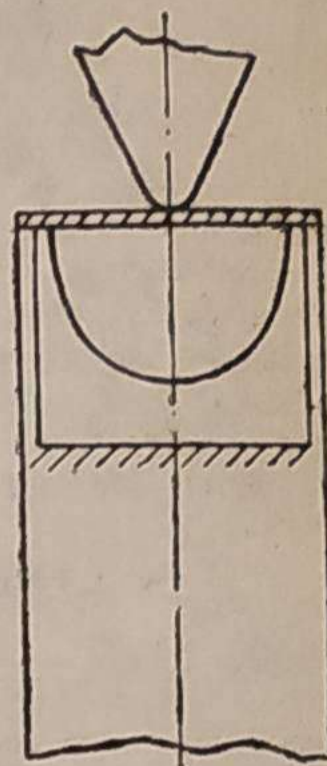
Оправка для изготовления полутрубы из листовой стали.
